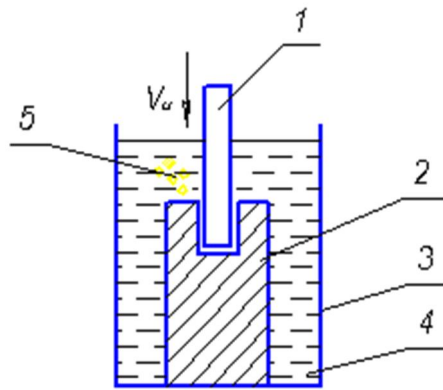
Схема прошивання отворів і порожнин: 1 – електрод-інструмент; 2 – заготовка; 3 – ванна; 4 – електроліт; 5 – продукти обробки; V_i – швидкість подачі інструмента
